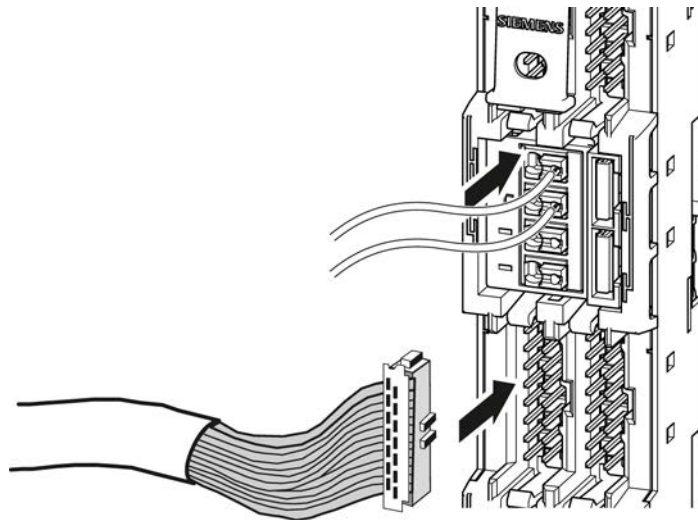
Leitungen für die Zuführung der Versorgungsspannung und Verbindungsleitungen am Frontsteckmodul anschließen (Beispielgrafik)
